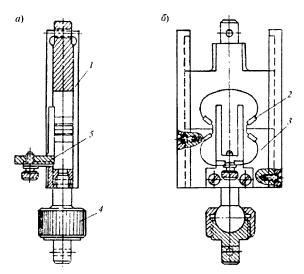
Приспособление для испытания образцов, имеющих форму восьмерок, на разрыв:
